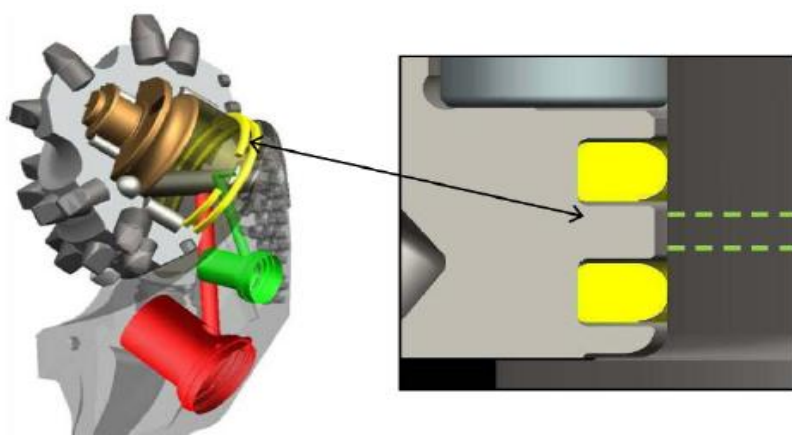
конструкция с двумя уплотнительными кольцами
